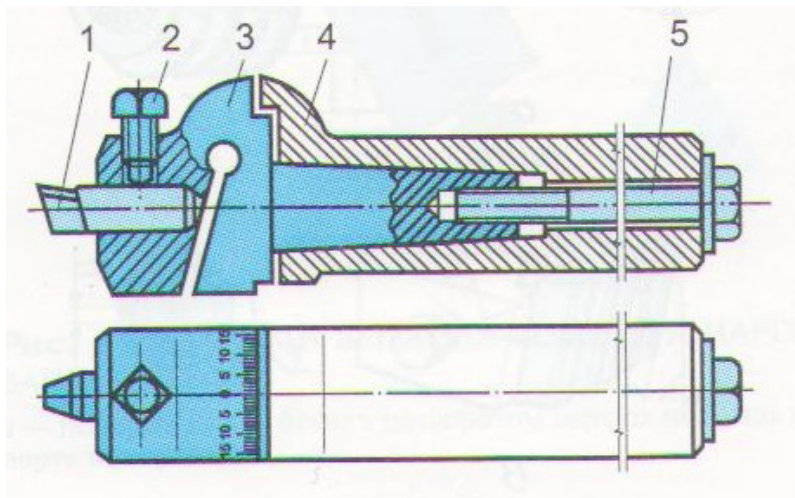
Державка з поворотною головкою для нарізного різця:
